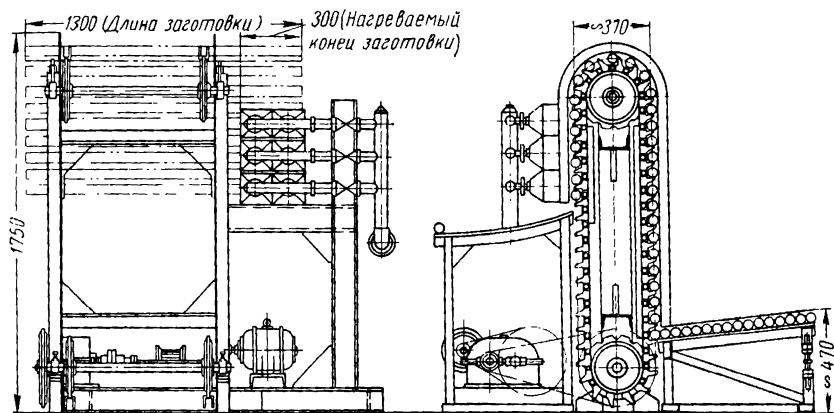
Установка для скоростного нагрева заготовок полуосей $d = 50$ мм под высадку. Температура нагрева 1150—1200° С; производительность 70 шт/ч; время нагрева 3 мин; топливо — природный или смешанный газ [10]
